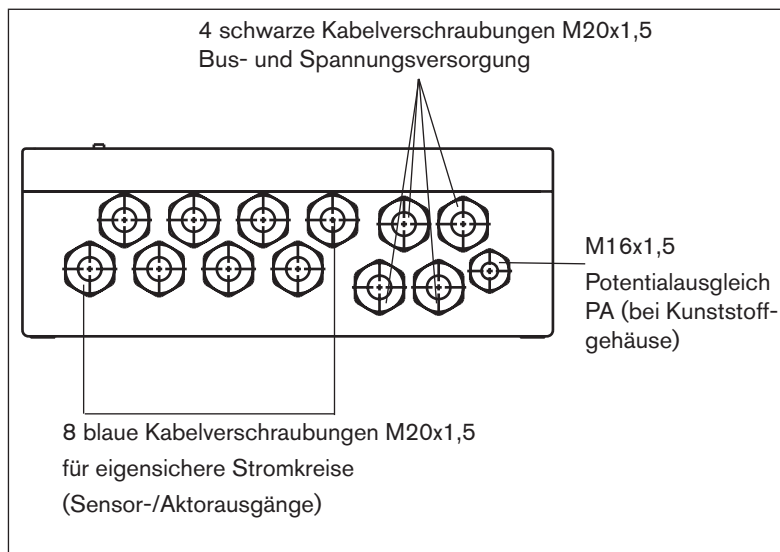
Kabelverschraubungen am Metallgehäuse
